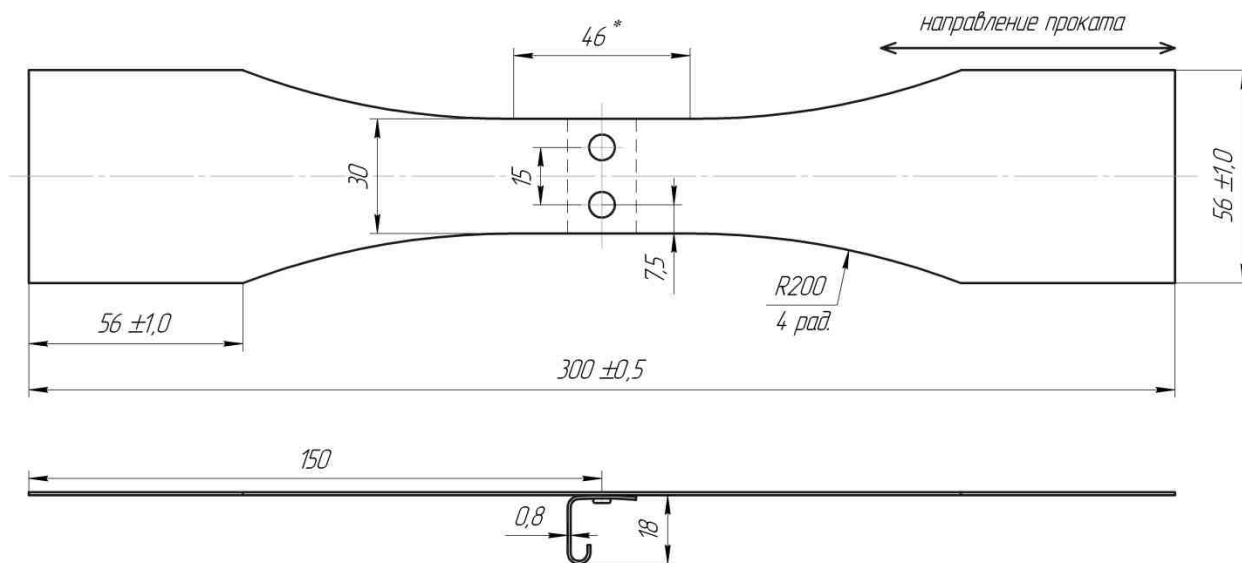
Фрагмент чертежа образцов с потайными заклепками
